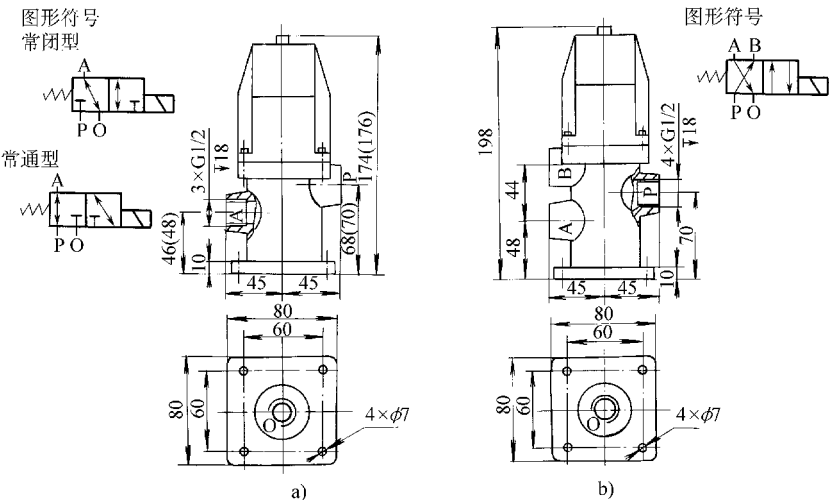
5-11 PC 系列二位三通、二位四通直动式电磁阀外形尺寸
